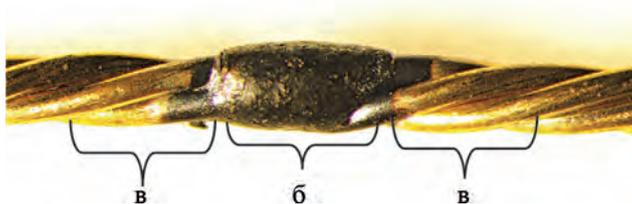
Зоны сварного соединения металлокорда: а – сварной шов; б – зона сплавления; в – зона термического влияния
